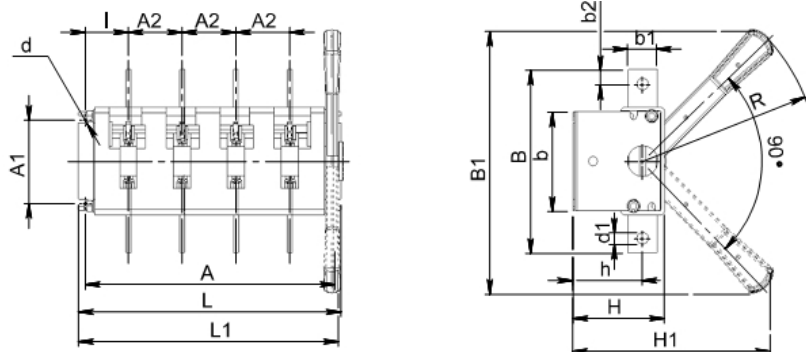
Б Выключатель-разъединитель на одно направление 4-полюсный с боковой рукояткой
